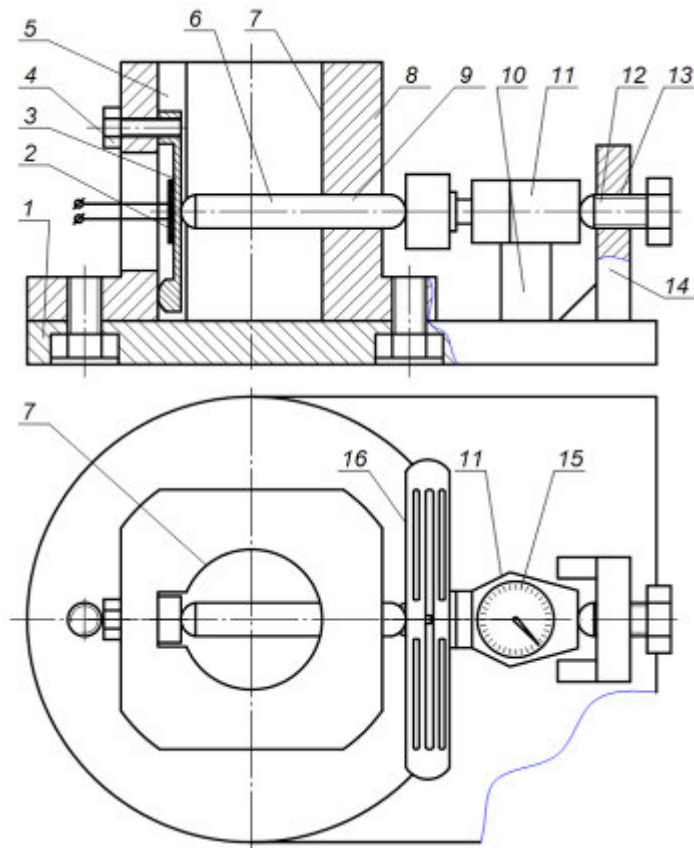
Спеціальний пристрій для тарування тензометричної балки
